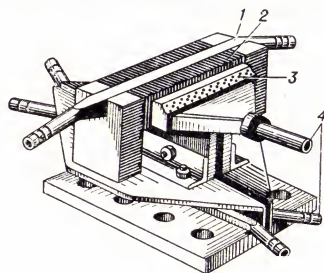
Индуктор для закалки плоской поверхности непрерывно-последовательным способом: 1 — индуктирующий провод; 2 — магнитопровод; 3 — душевое устройство для подачи закалочной воды; 4 — трубопровод водяного охлаждения.
